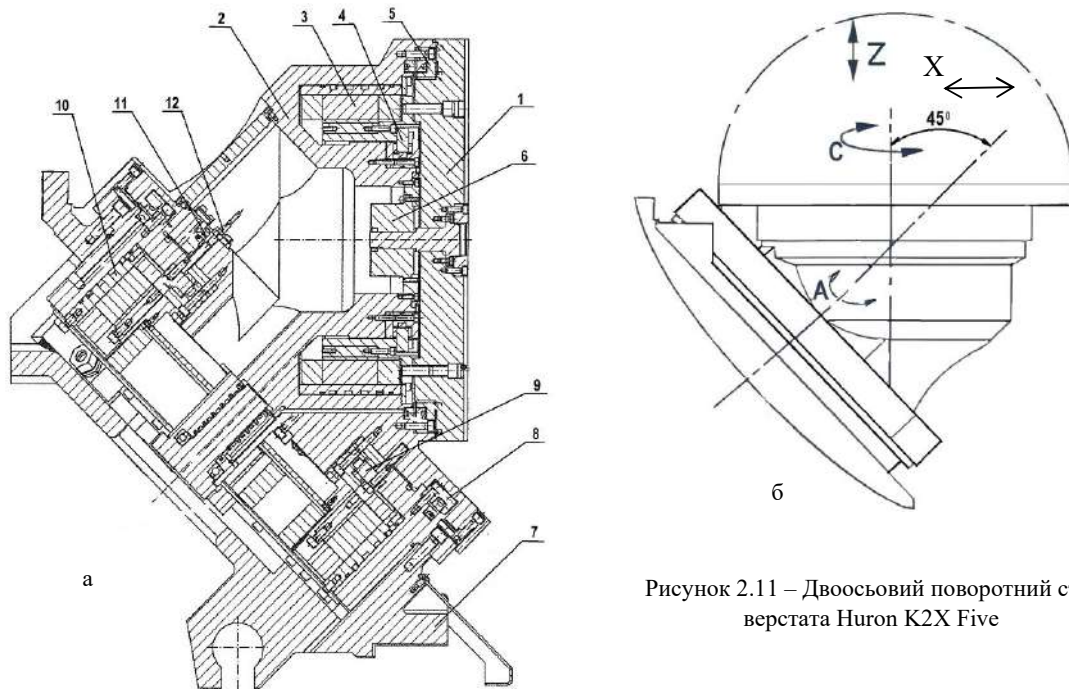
Двоосьовий поворотний стіл верстата Huron K2X Five
